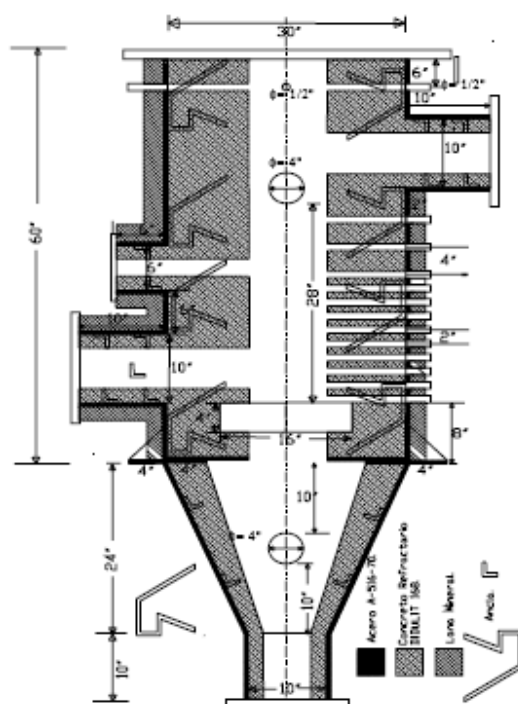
Vista frontal de la planta y gasificador de biomasa de la planta del Instituto de Ingeniería de la UNAM
